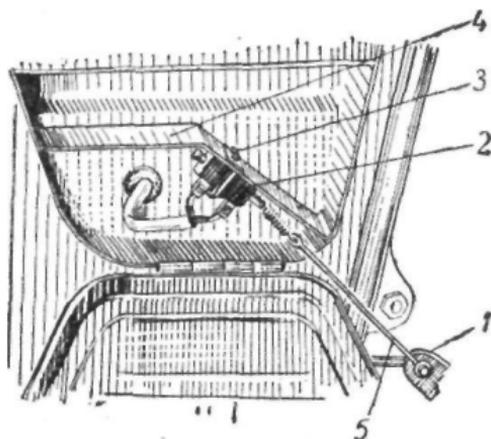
Установка включателя стоп-сигнала ИЖ сб. 38—0:
